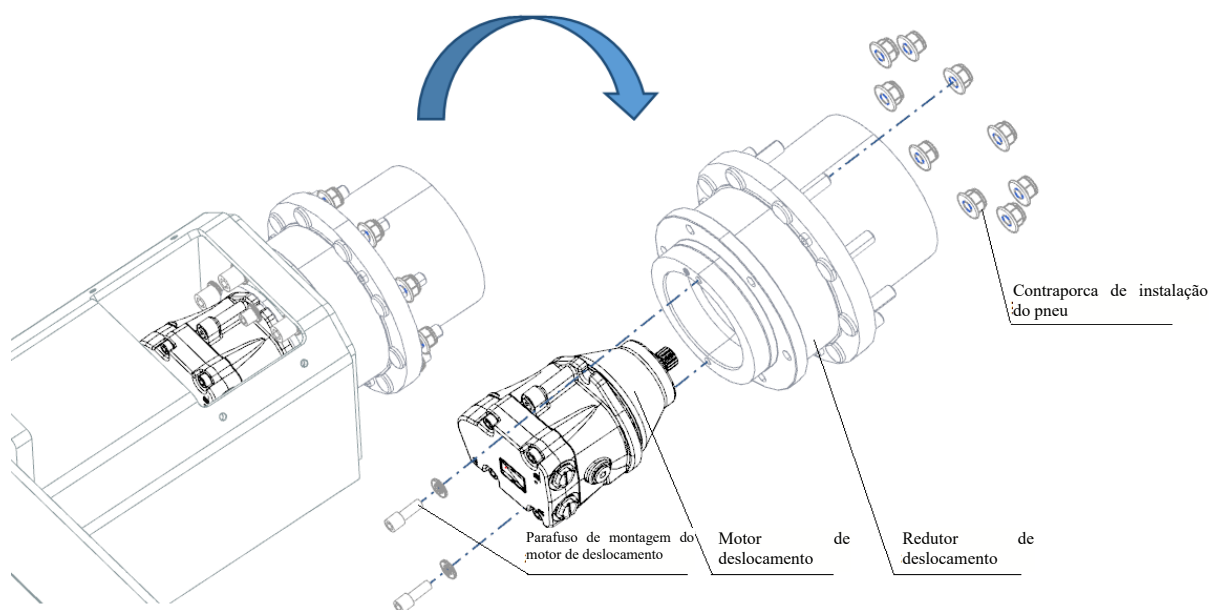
Diagrama de desmontagem do motor de deslocamento
